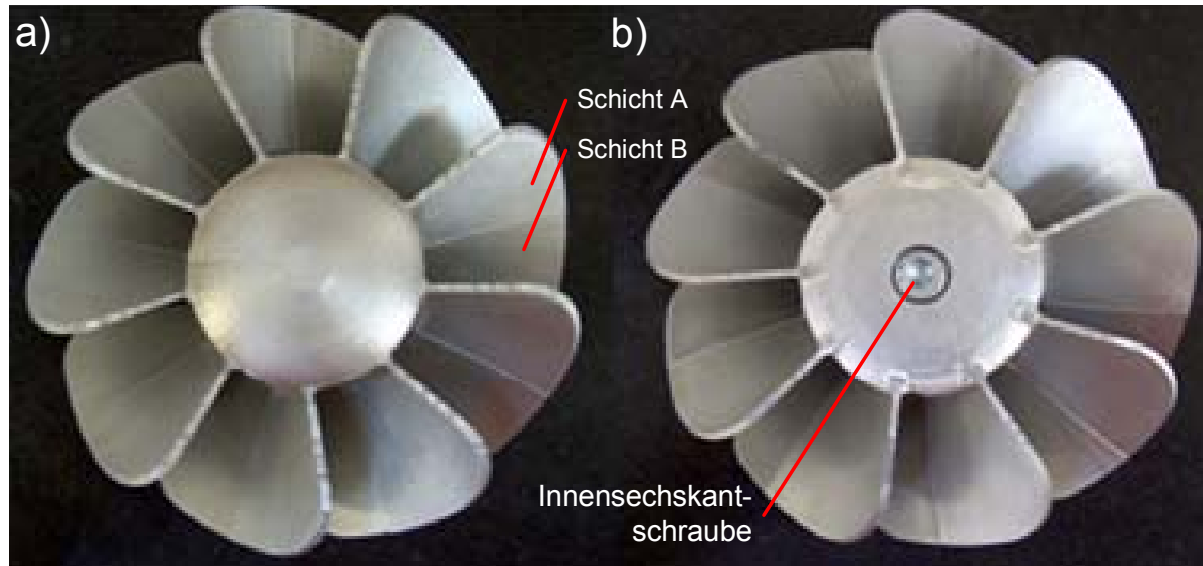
gefügter Probekörper: a) Draufsicht b) Unteransicht
